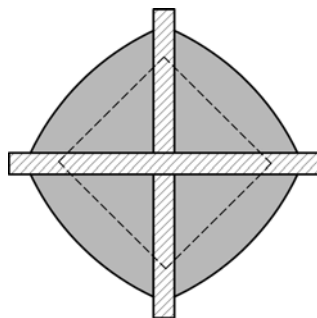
Поперечний переріз деталі для виготовлення зразка зварного шва
